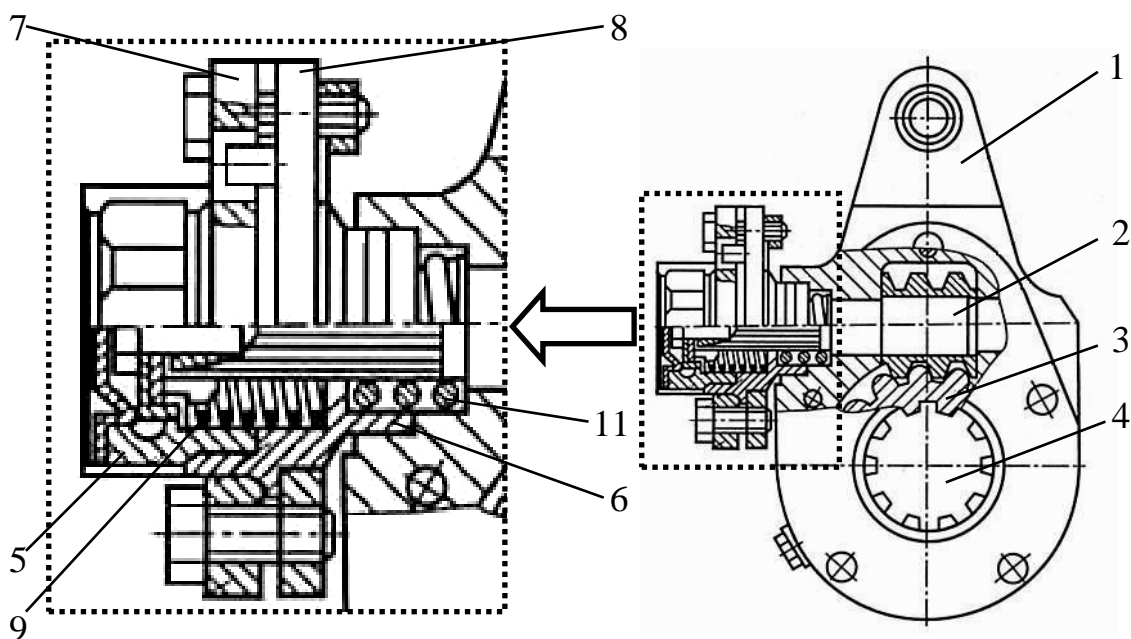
Устройство автоматической регулировки зазора между тормозными колодками и барабаном тормозного механизма с кулачковым разжимным устройством: 1 – корпус рычага регулировочного устройства; 2 – вал с червяком; 3 – червячное зубчатое колесо; 4 – вал кулачка разжимного устройства тормозного механизма; 5 – гайка; 6 – корпус муфты; 7 – скоба, 8 – установочное кольцо; 9 – блокирующая пружина из проволоки прямоугольного сечения; 10 – шток тормозной камеры; 11 – фиксирующая пружина
